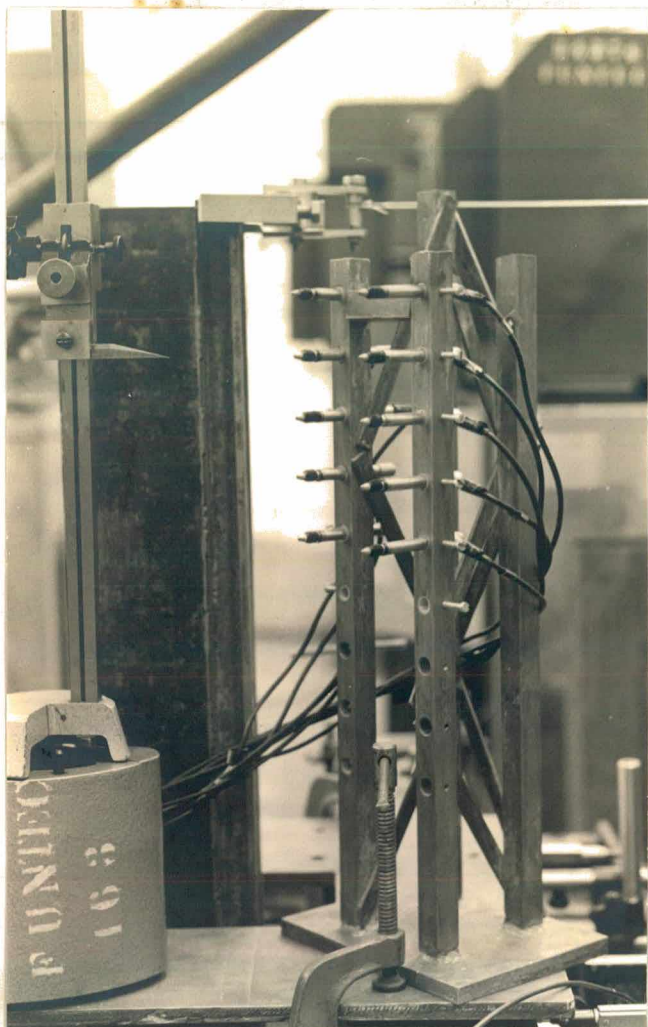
(a)- Aspecto construtivo do suporte de medição
